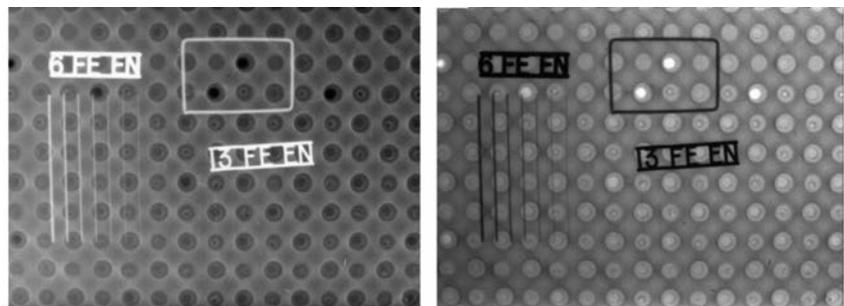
Цифровые изображения образца с двойной точечной сваркой с локализацией участка для исследования с помощью твердотельного преобразователя S10811-11: а – негатив; б – позитив
